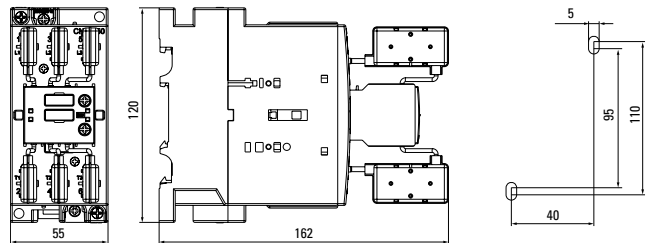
Габаритные и установочные размеры контакторов КМЭК 40, 50
